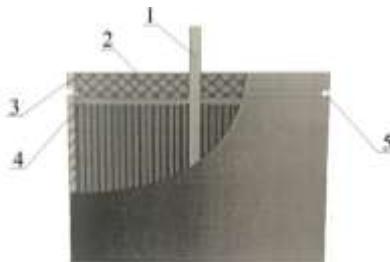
Конструкція плівкового конденсатора: 1 – вивід; 2 – компаунд; 3 – корпус; 4 – перегородка; 5 – штампування в корпусі
